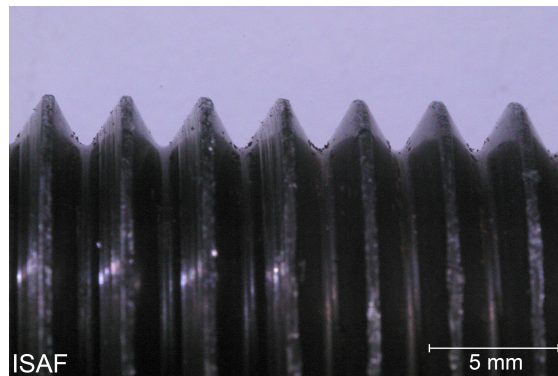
Gewindeprüfkörper axial belastet mit 60kN (Bolzen)
